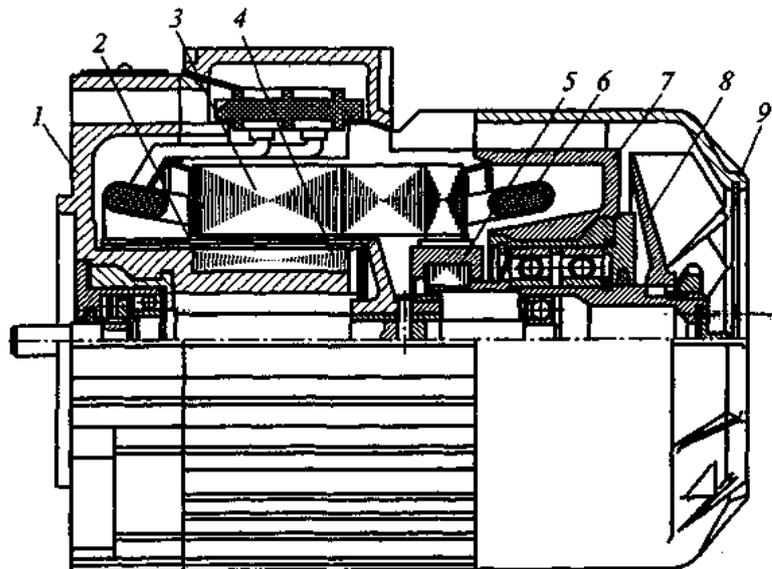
Асинхронный исполнительный двигатель типа ДАУ-63П ($P_n = 63$ Вт; $n_n = 2500$ об/мин) с двумя роторами:
